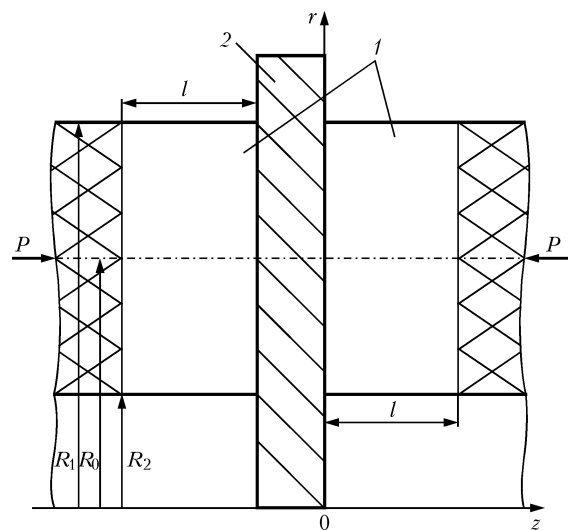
Расчетная схема процесса сварки полиэтиленовых труб: 1 — исходные заготовки; 2 — нагревательный инструмент
